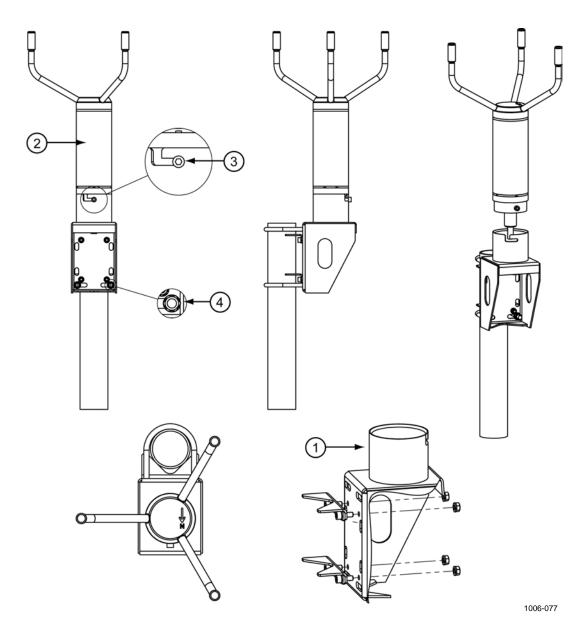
Установка датчика ветра WMT700 сбоку мачты
